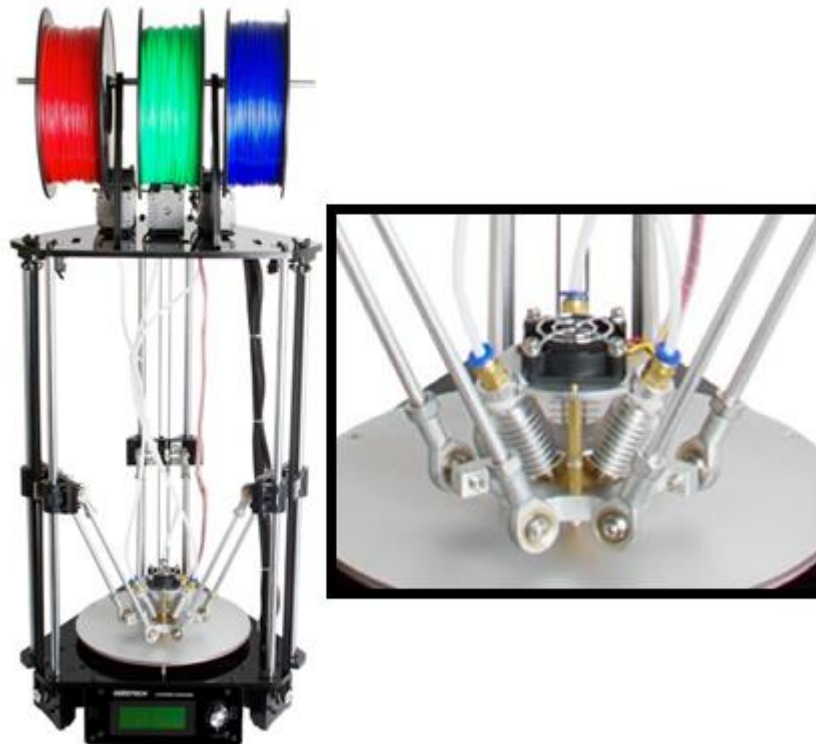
Impressora 3D *Geetech Delta 301* e pormenor do *Diamond extruder* (adaptado de [18]).
